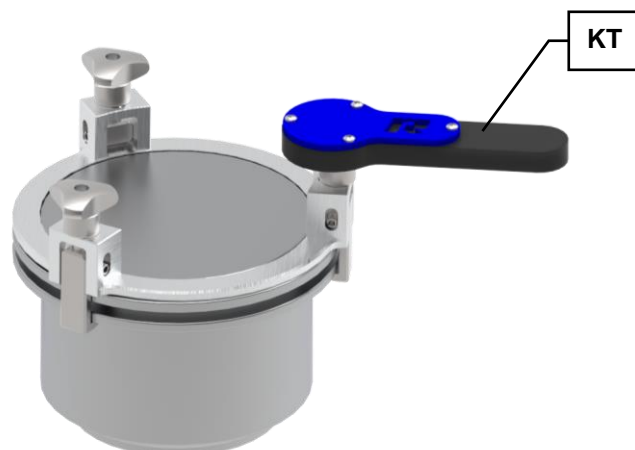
Затягивание запорного устройства с помощью вспомогательного приспособления для открывания и закрывания
